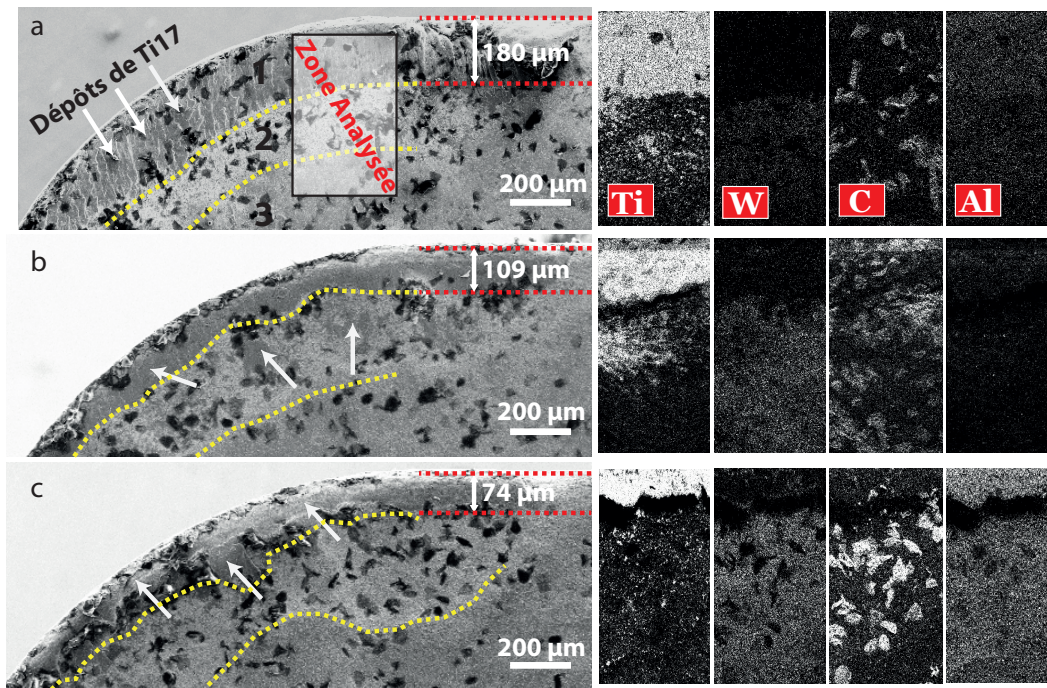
Analyse des dépôts de matière sur la face de coupe des outils après 15 min d'usinage en finition : (a) usinage conventionnel (b) P=100 bar et (c) P=250 bar
